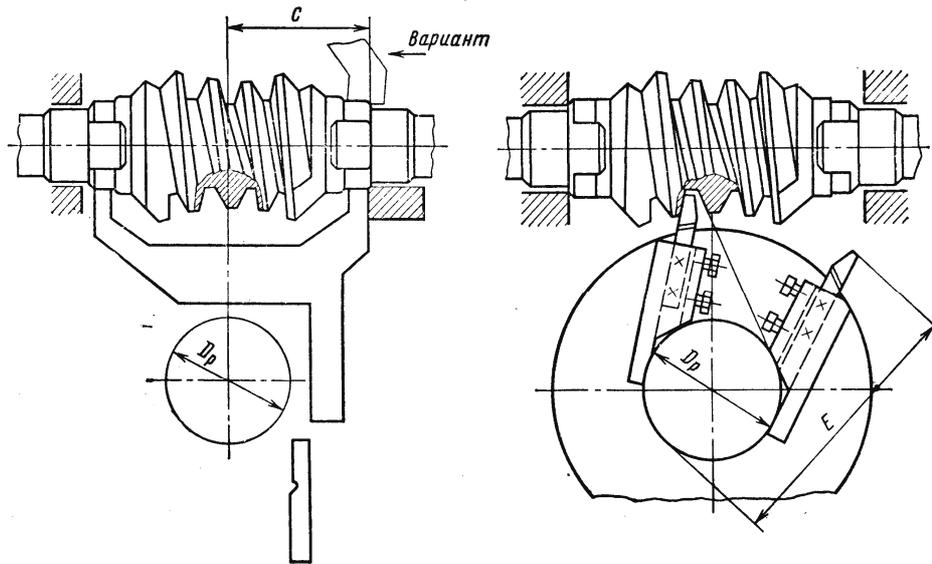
Установка червяка по центру глобоида и нарезание глобоидного червяка резцами
